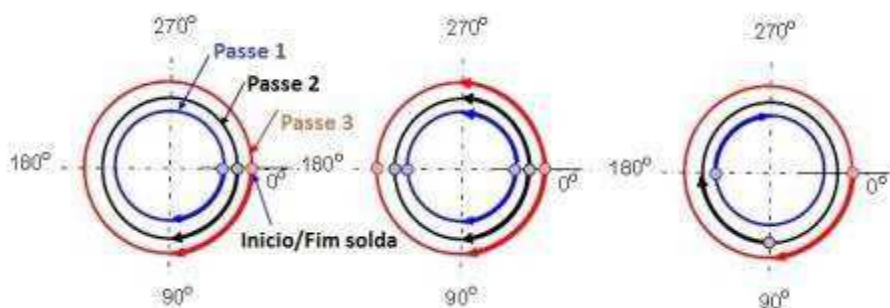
Sequências de soldagem (Adaptado DENG, 2013).
